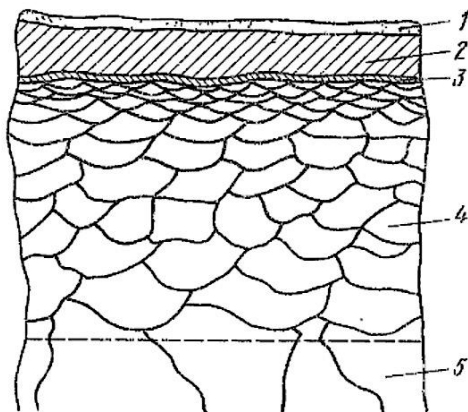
Схема поверхностного слоя детали [8]:
